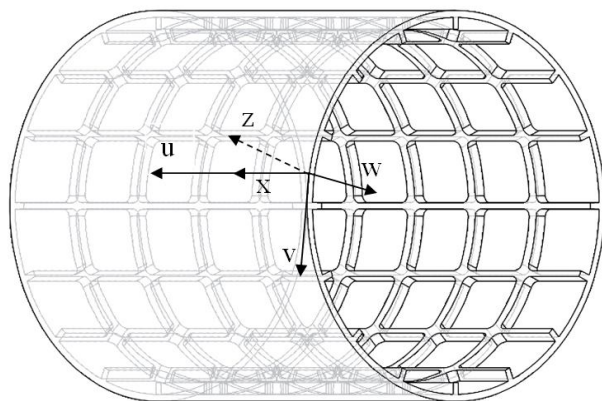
Эскиз несущей цилиндрической оболочки бака ракеты
